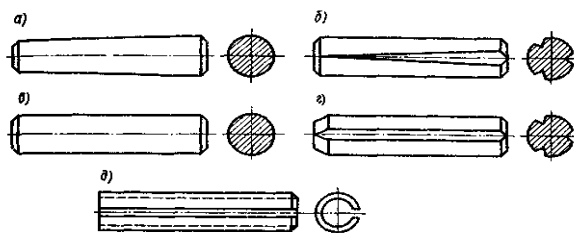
Основні види конструкцій штифтів: а) конічний гладкий; б) конічний з насічками; в) циліндричний гладкий; г) циліндричний з насічками; д) пружинний
